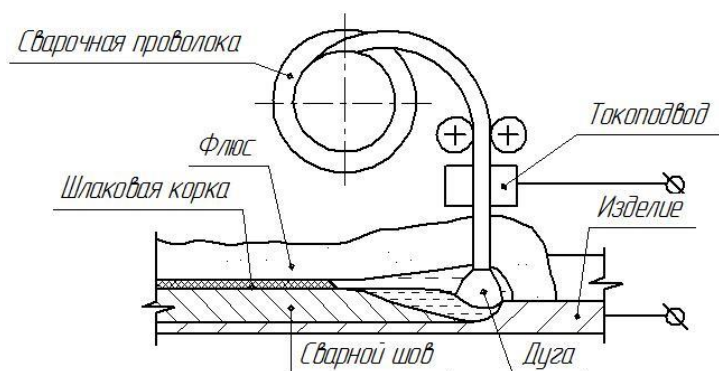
Схема автоматической сварки под флюсом
